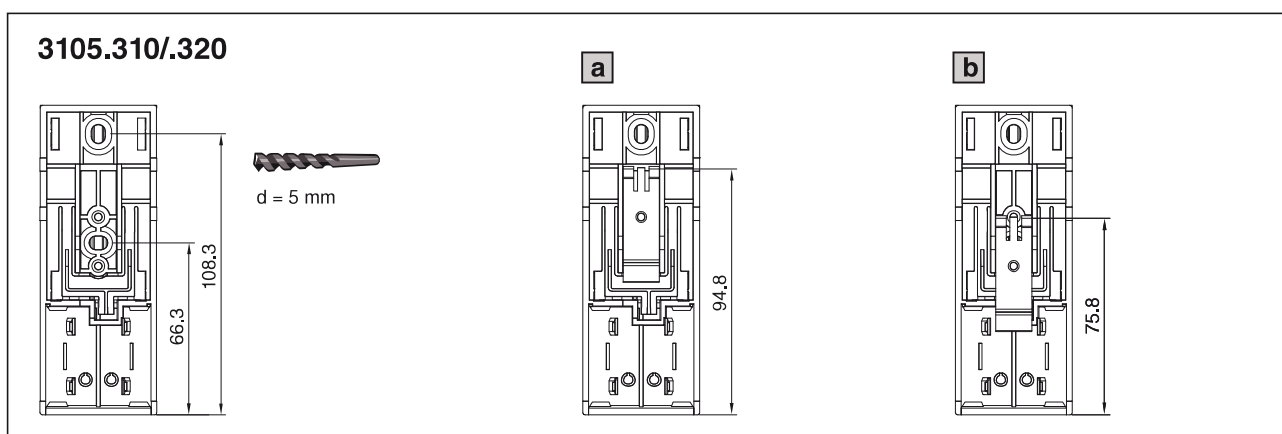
Fixation sur plaque de montage / Possibilités de fixation sur rail porteur
